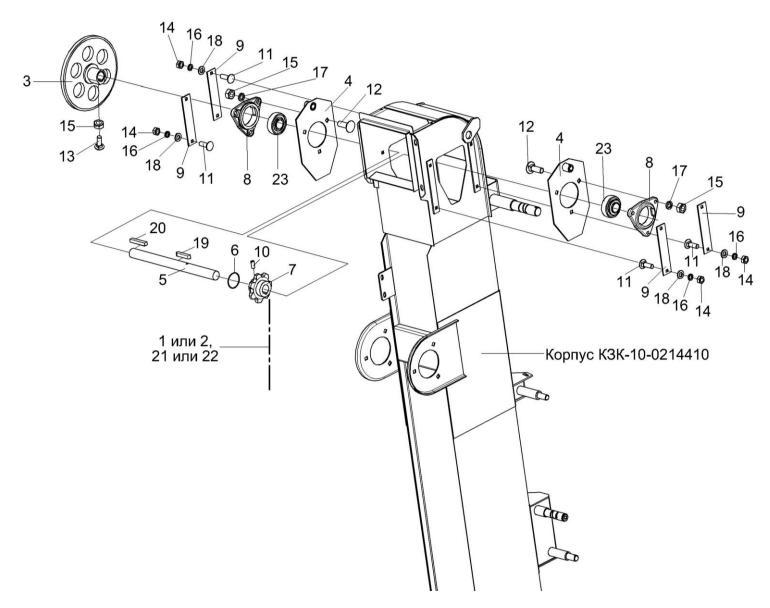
Элеватор зерновой КЗК-10-0214000 (лист 2)
